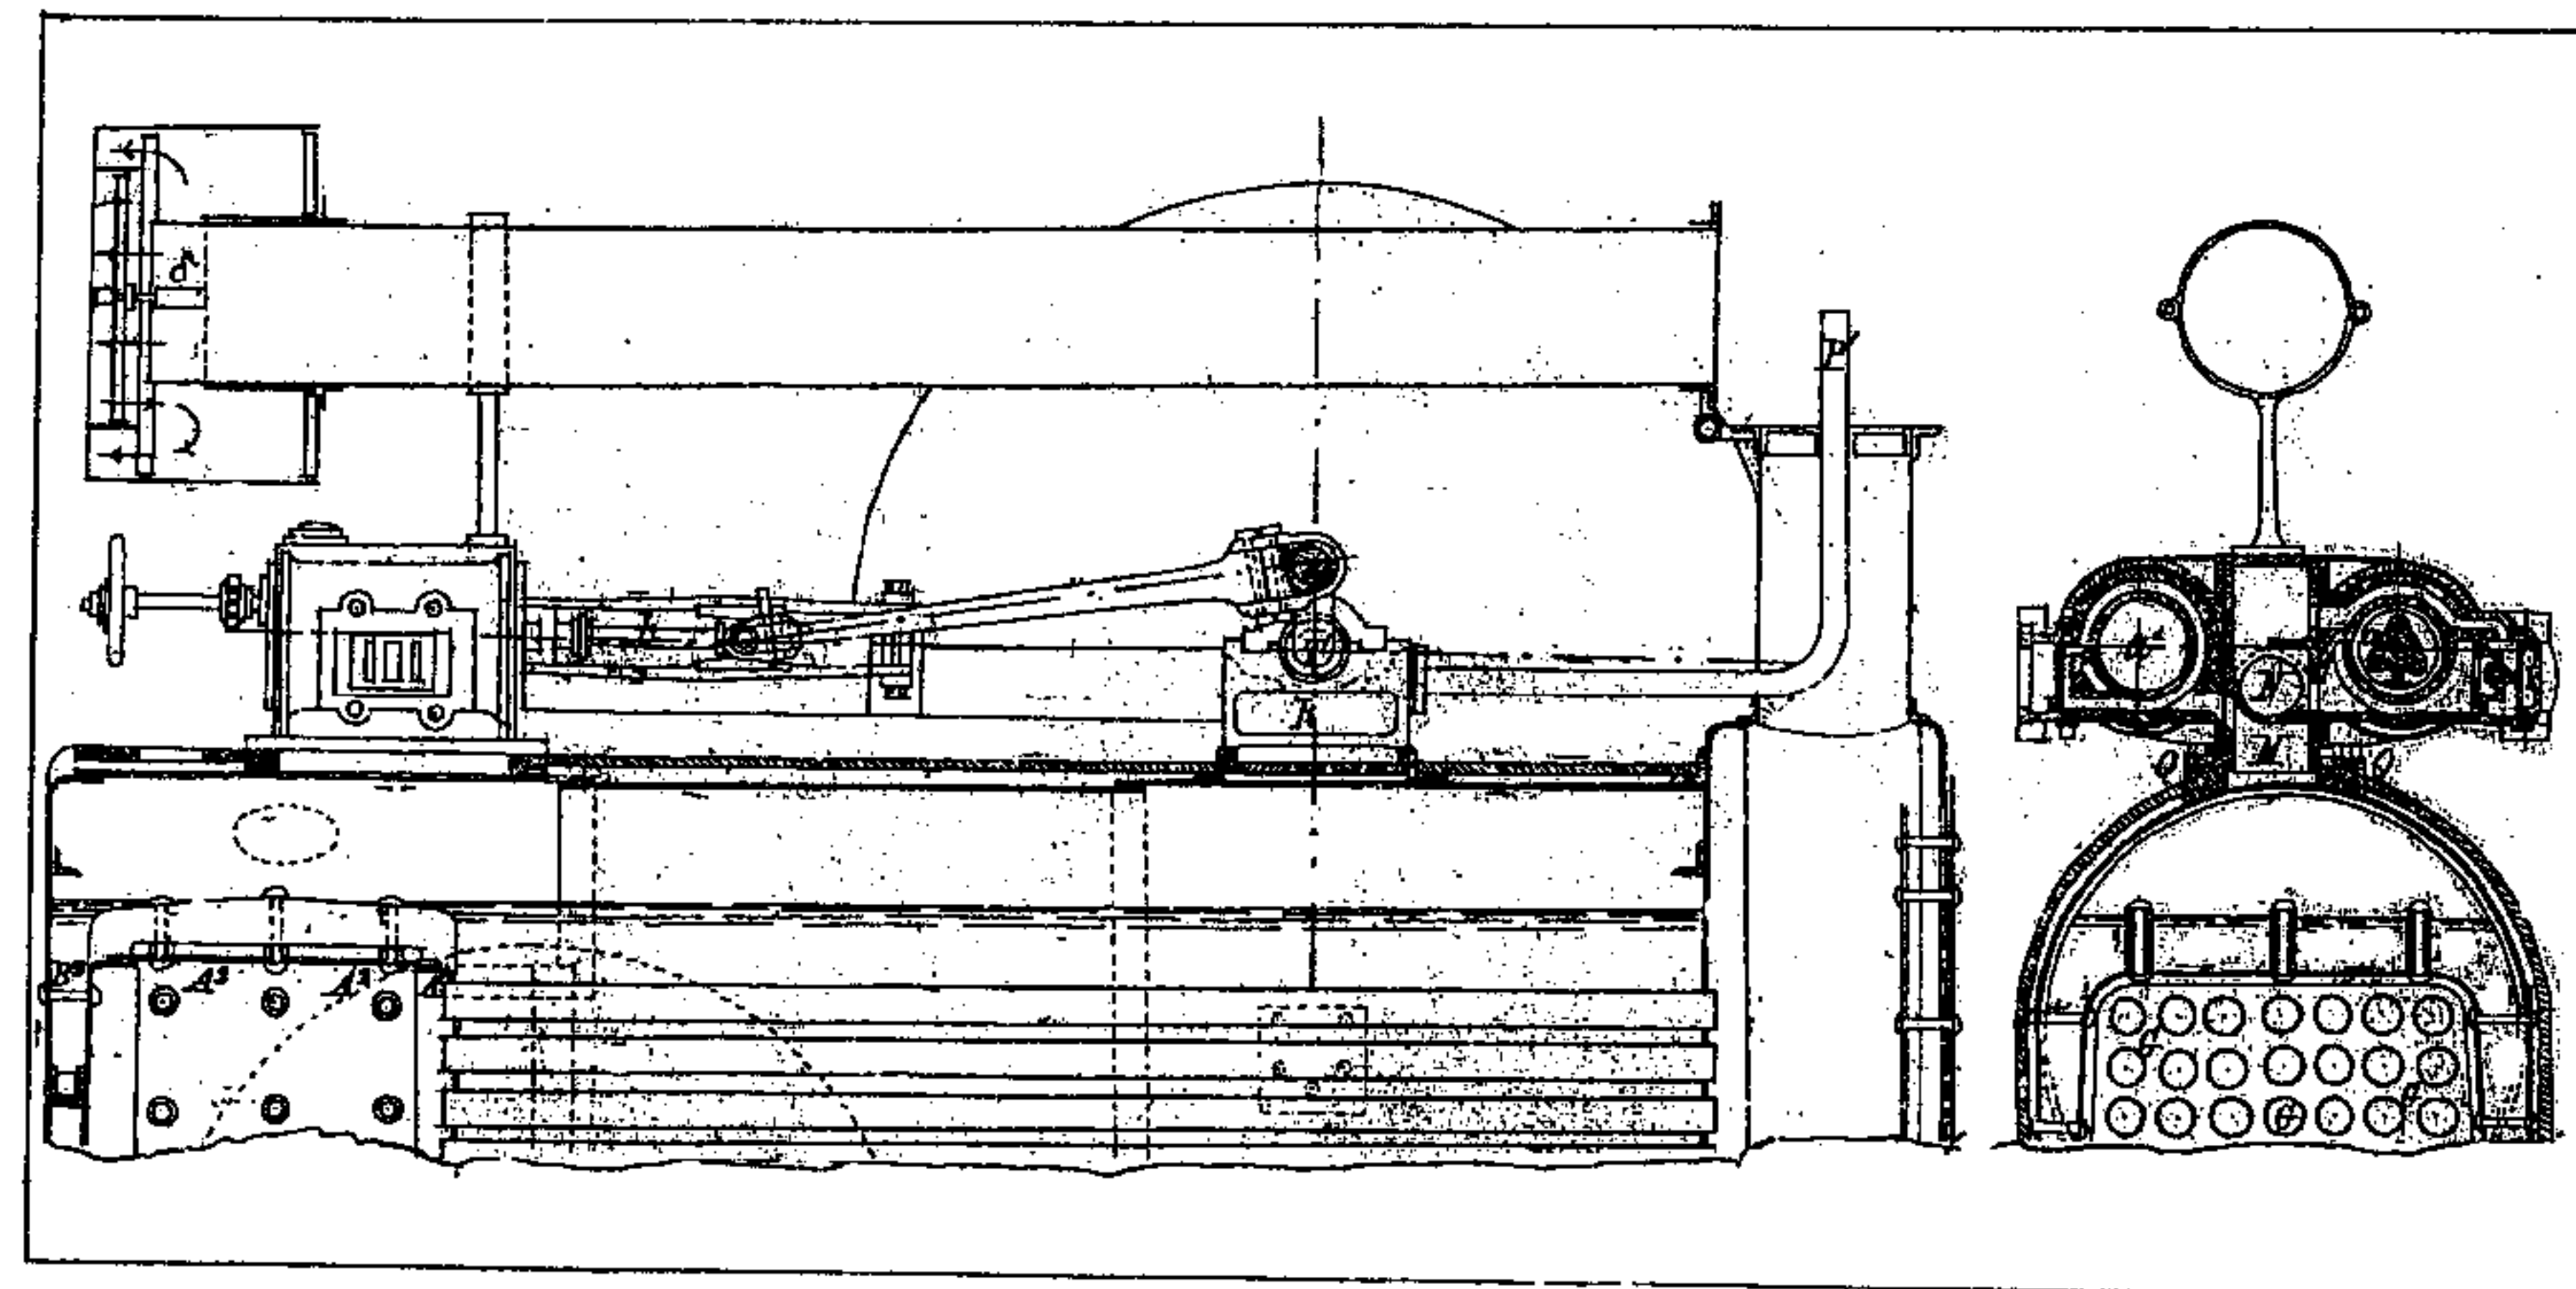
/6: Skizze der Lokomobilmaschine von Egestorff (1865)
